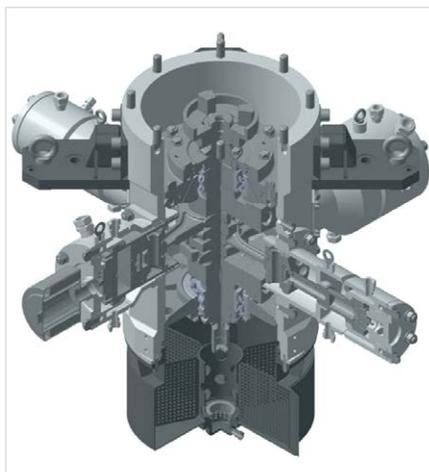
Разрез четырехрядного компрессора с вертикальным коленчатым валом
